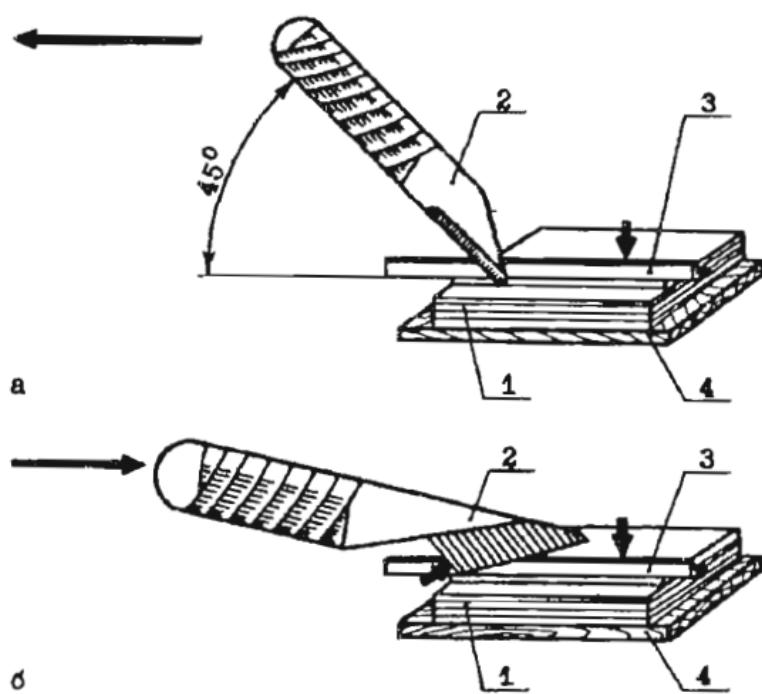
Обрезка книжного блока универсальным переплетным ножом: а - прием обрезки движением ножа к себе; б - прием обрезки в направлении от себя; 1 - книжный блок; 2 - универсальный нож; 3 - металлическая линейка (фальцлинейка); 4 - подкладная доска
